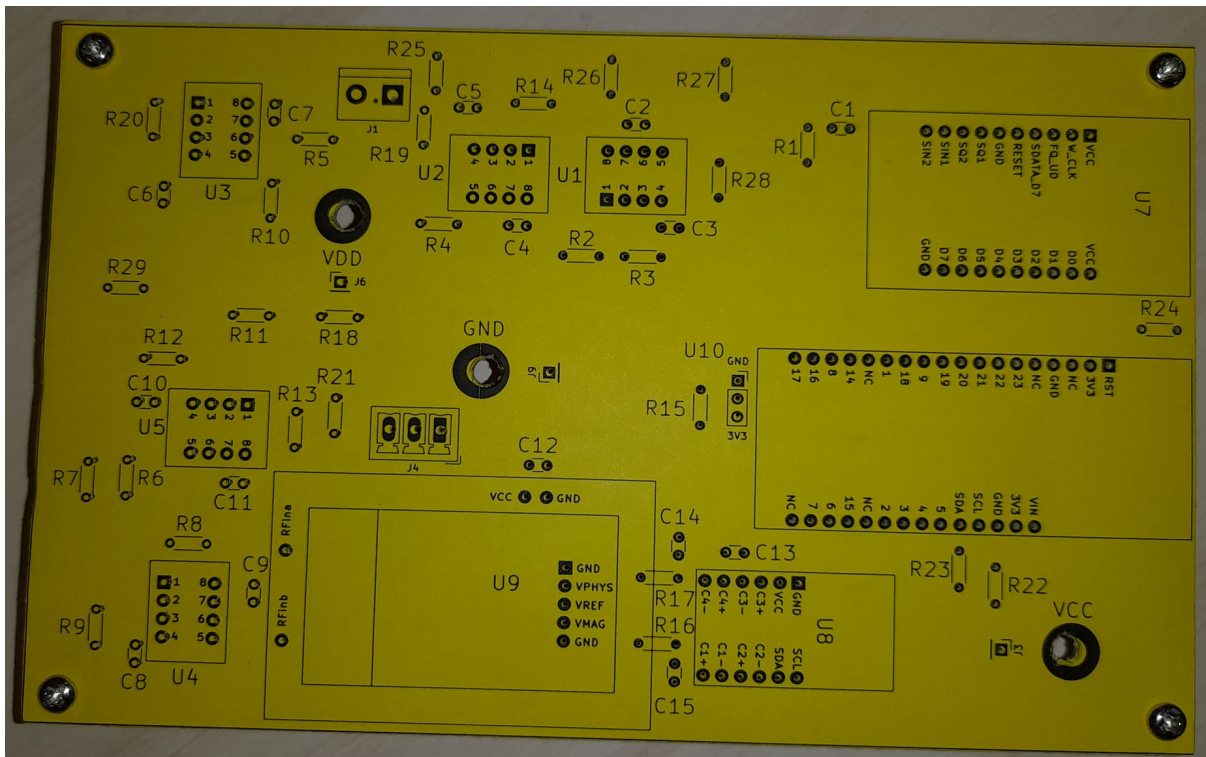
Σχεδιασμός PCB στο KiCad
